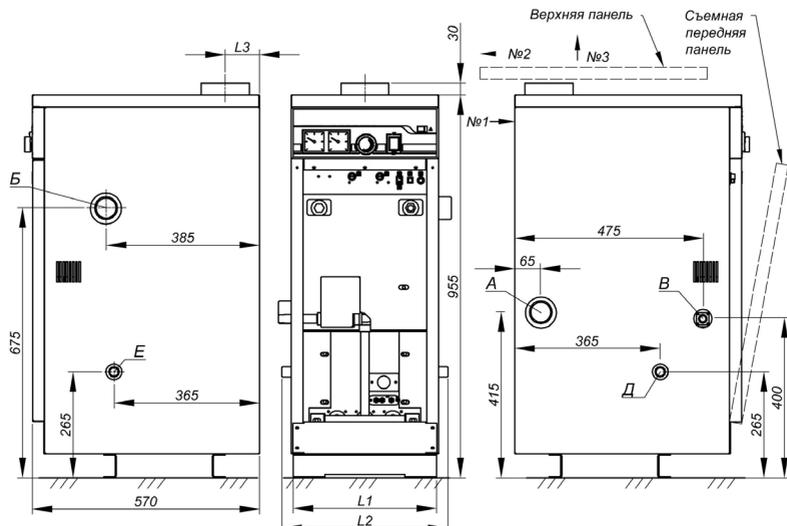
Габаритные и присоединительные размеры котла ALFA COMFORT E
